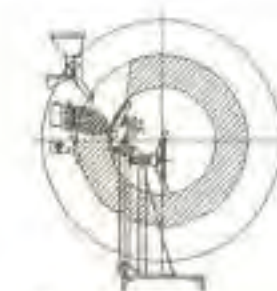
Зварювання вала з застосуванням внутрішнього ковзуна
